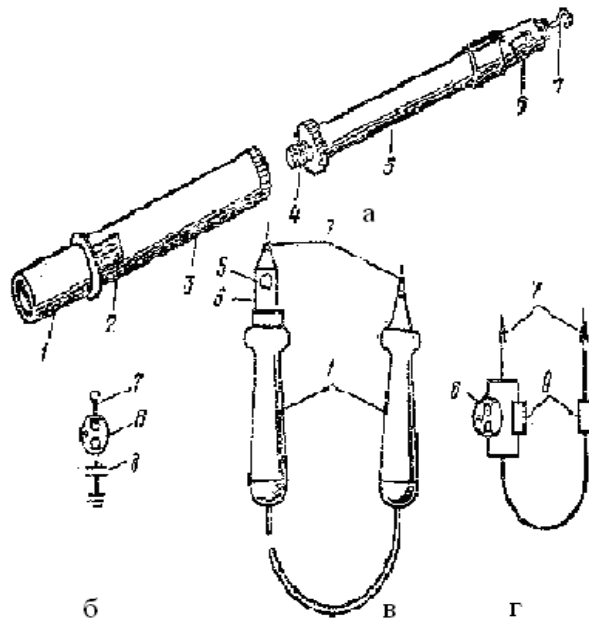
Устройства и схемы указателя высокого напряжения УВН-80 (а и б) и токоискателя низкого напряжения ТИ-2 (в и г): 1 – рукоятка; 2 – штамп с датой следующего испытания; 3 – изолирующая часть; 4 – винтовой металлический разъем; 5 – рабочая часть; 6 – сигнальная лампа; 7 – металлический щуп (наконечник); 8 – конденсатор; 9 – резистор
